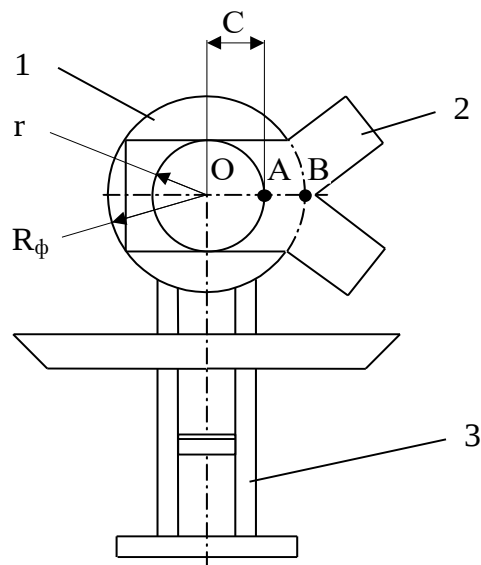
Розрахункова схема: 1 – фланець планшайби; 2 – двигун;
